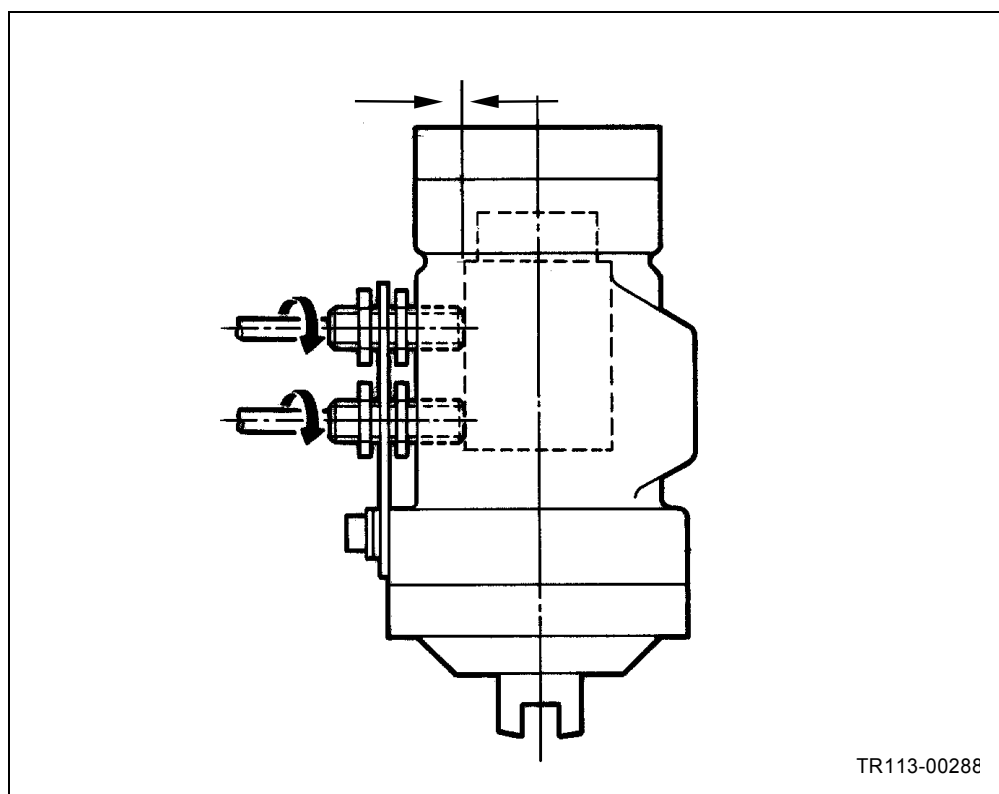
Процедура регулировки фрезерного соединения (2/2)
